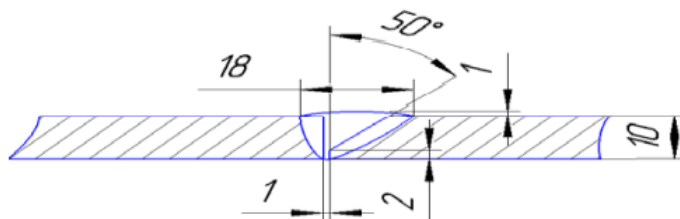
Ескіз стикового зварного з'єднання для зварювання поздовжнього стику шва обичайки
